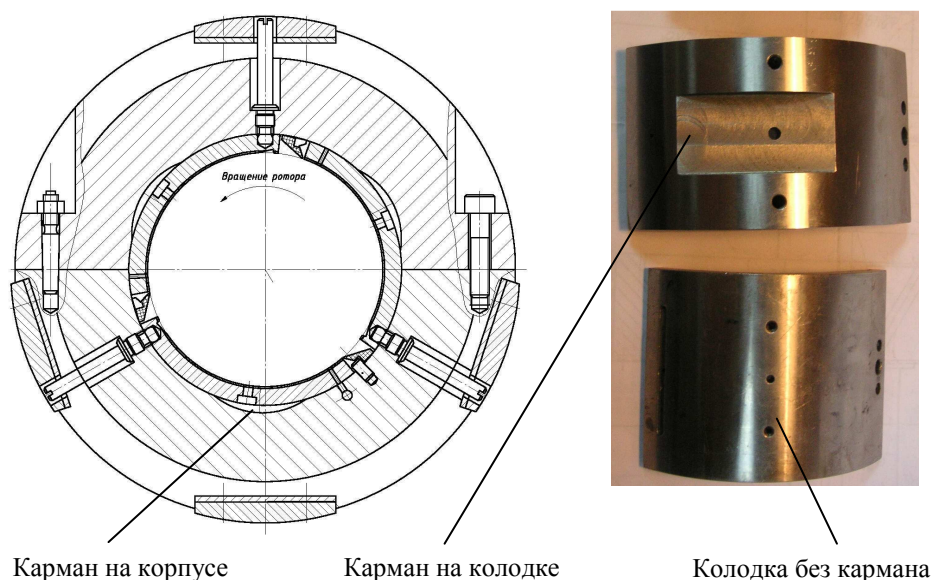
Демпферный опорный подшипник с карманом на корпусе
